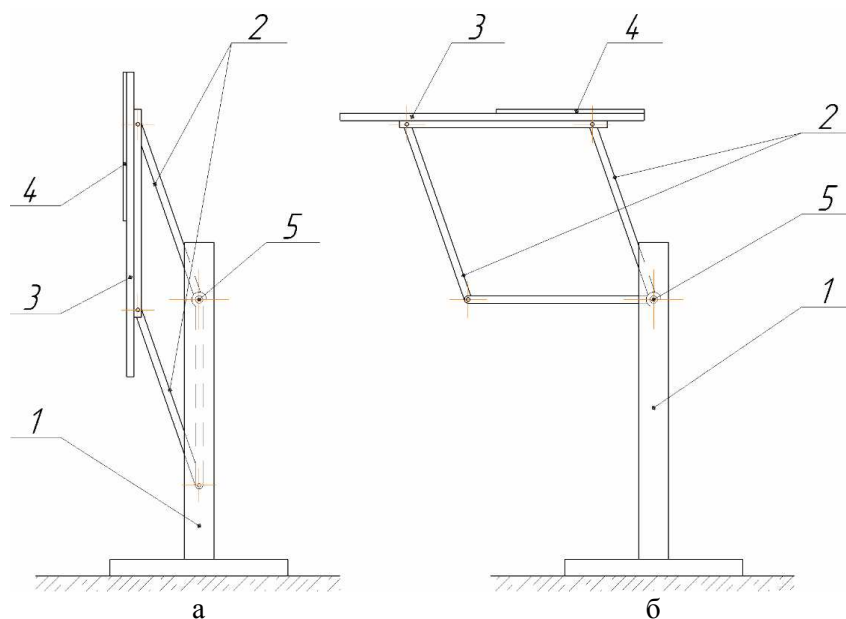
Лабораторная установка: а) рабочая поверхность повернута на 90° к опорной поверхности; б) рабочая поверхность параллельна опорной поверхности; 1 – рама; 2 – рычажный механизм; 3 – рабочая поверхность; 4 – рассматриваемый материал; 5 – ось
